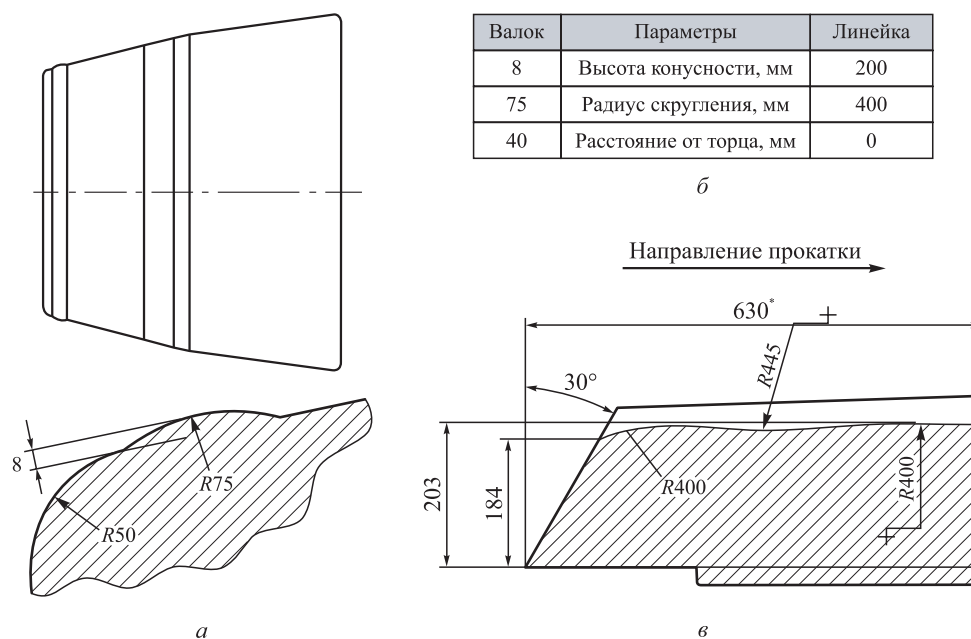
Параметры гребня на валке и линейки: чертеж валка с гребнем (а); основные параметры (б); чертеж линейки с конусностью (в)
